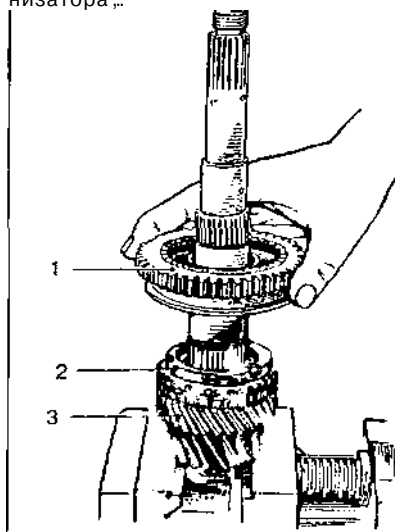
Снятие ступицы третьей и четвертой передач с ведомой шестерней заднего хода: 1 — шестерня ведомая заднего хода; 2 — кольцо синхронизатора; 3 — шестерня ведомая четвертой передачи.
